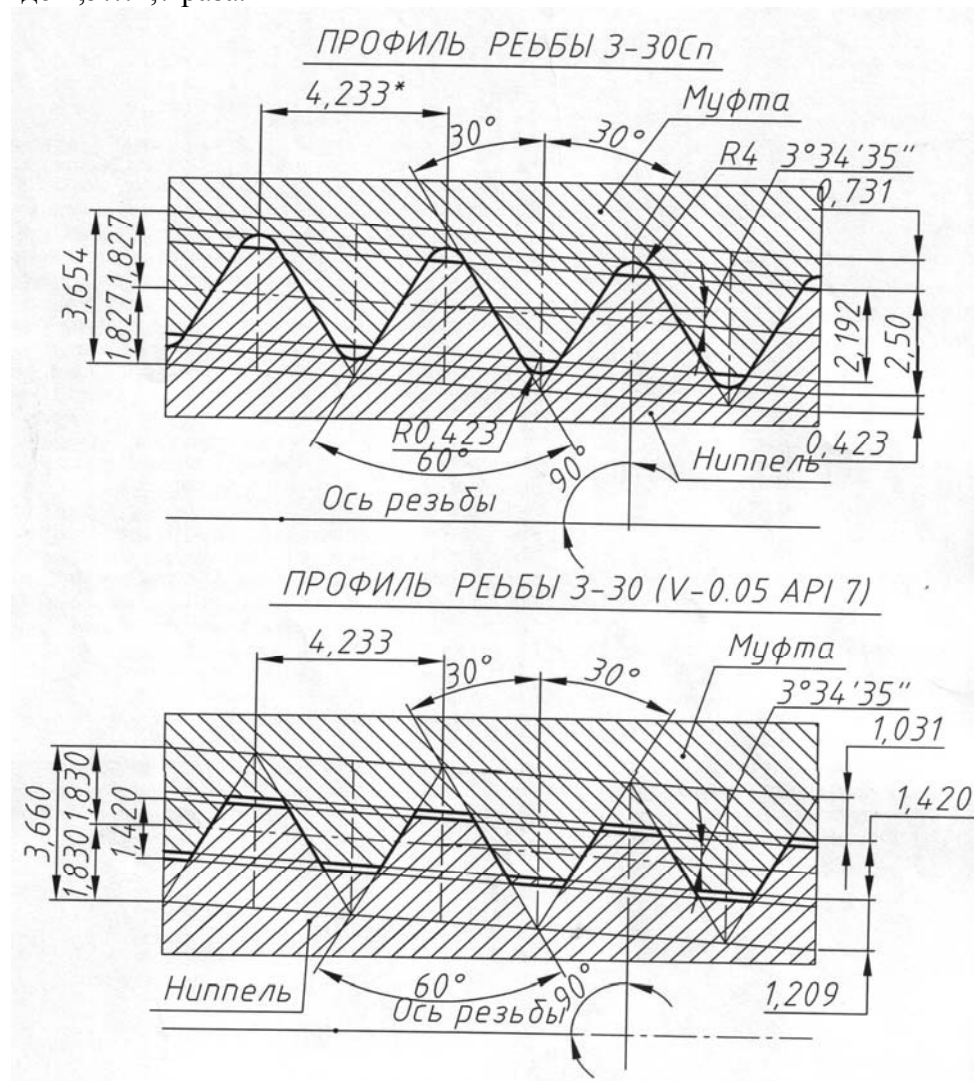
Типы замковых резьб для штанг малого диаметра
